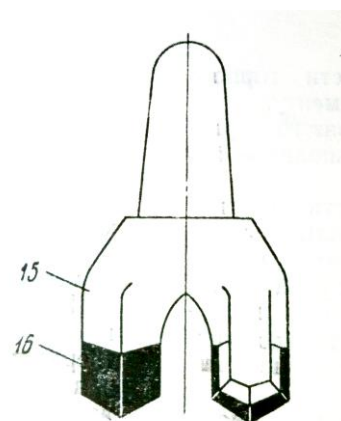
Схема резца для вращательного бурения с клиновидной рабочей частью [4]
